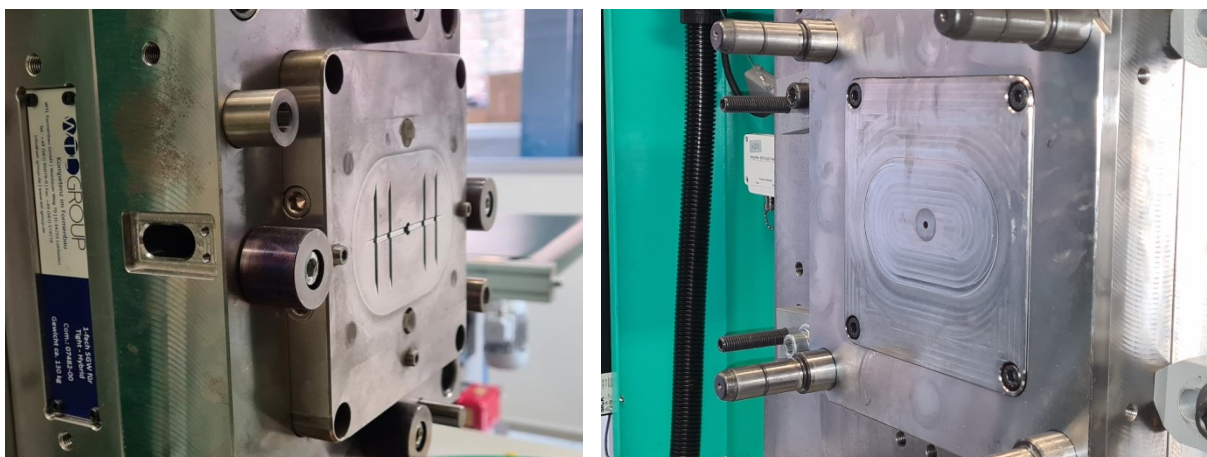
Formeinsätze mit 2d-Hybridbauteilgeometrie im eingebauten Zustand auf Spritzmaschine
